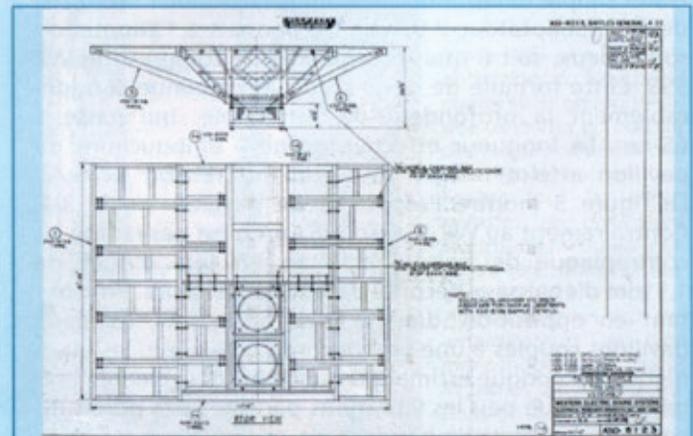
Plan original du baffle plan Western Electric TA-7396. Il avait été conçu pour recevoir une paire haut-parleurs de 46 cm TA-4181A.
